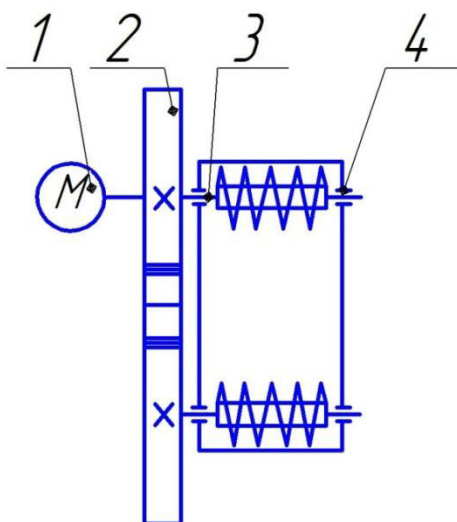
Кінематична схема приводу ЗБФА: 1. - Мотор-редуктор; 2. - Зубчаста передача; 3. – Вал зі шнеком; 4. - Підшипникова опора.
